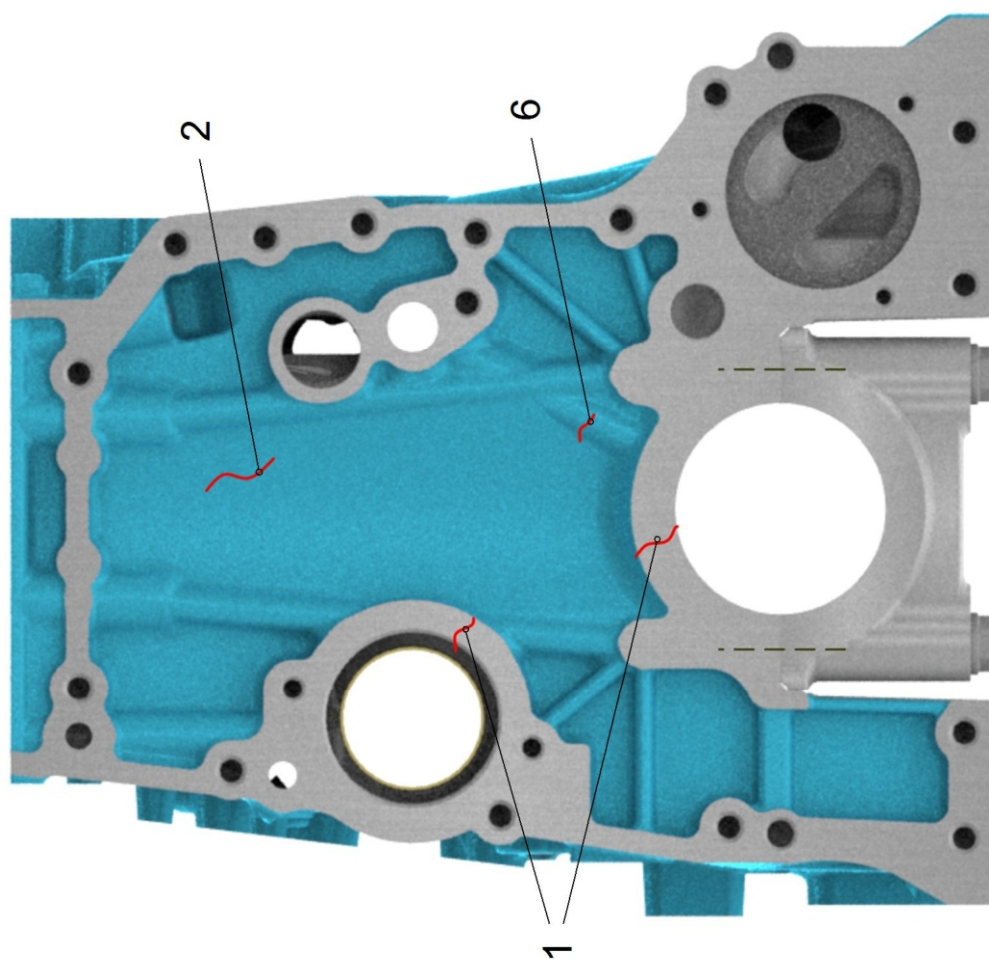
Блок цилиндров (Лист 1 из 5)
